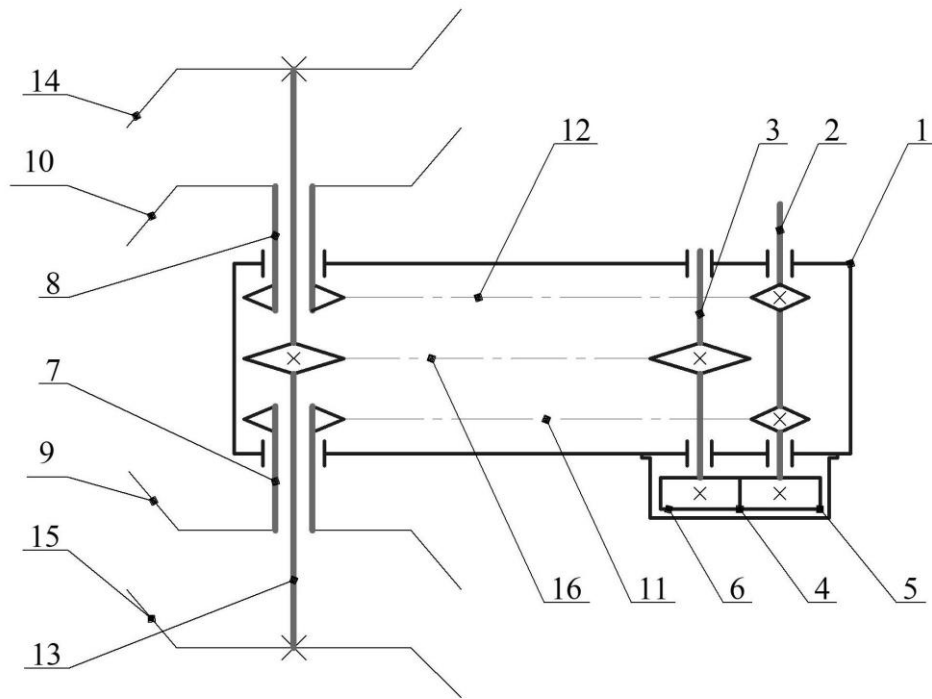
Принципиальная схема двухроторной почвообрабатывающей фрезы
